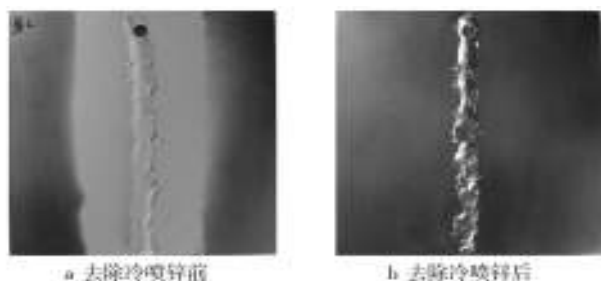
焊接件焊缝部位冷喷锌保护后形貌和电动钢丝刷去除冷喷锌后形貌
